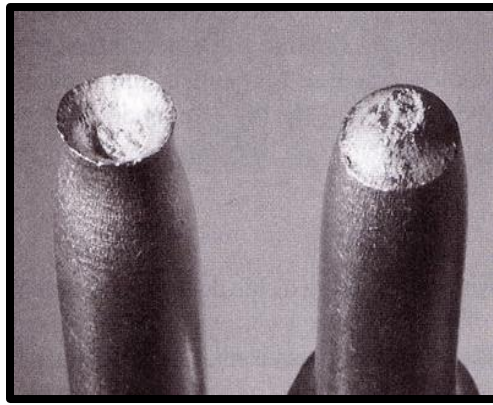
Fractura dúctil a tensión en tornillo [IDDP].
